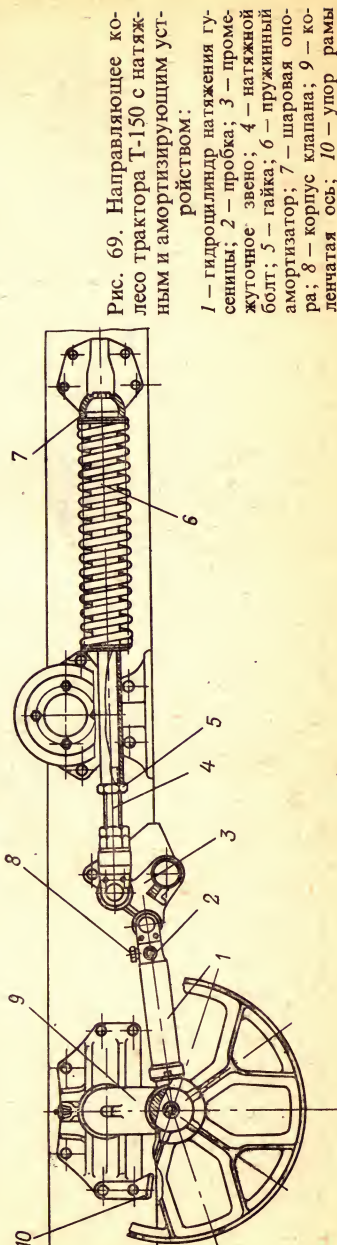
Направляющее колесо трактора Т-150 с натяжным и амортизирующим устройством:
